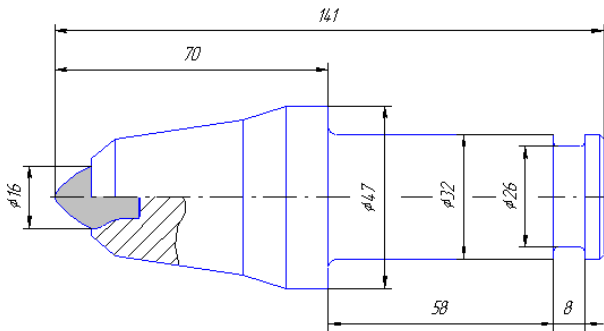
Тангенциальный поворотный резец РШ 32-70/16SK с грибовой твердосплавной вставкой
